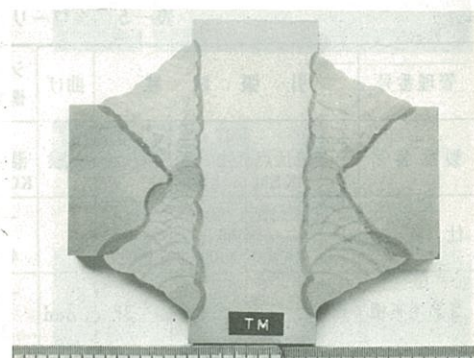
ピンプレートとブラケットとの溶接施工性試験体の断面マクロ
